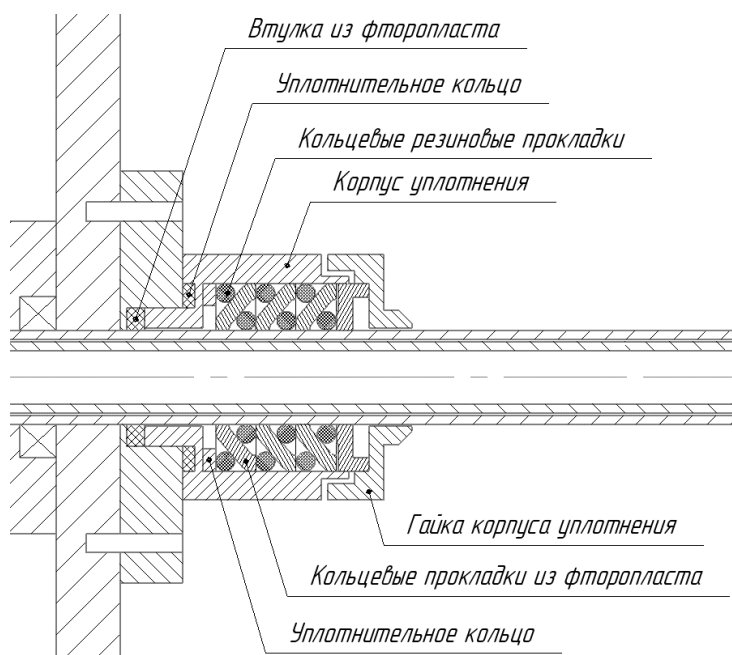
Общий вид механизма для обеспечения герметичности в разрезе
